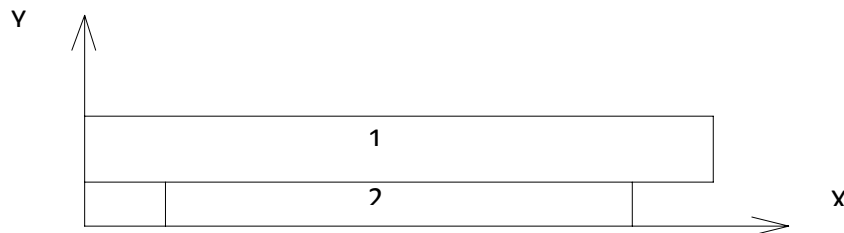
Sección de la llanta y forma en que se divide para el cálculo.
